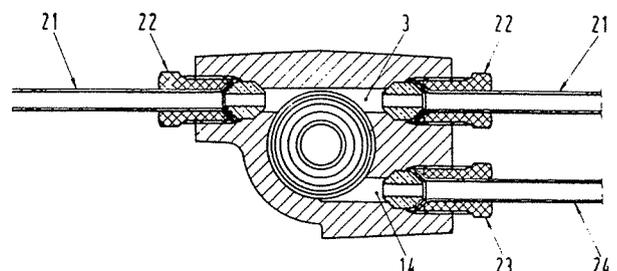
Schnitt durch die Bremsleitungsanschlüsse am Hauptbremszylinder.
